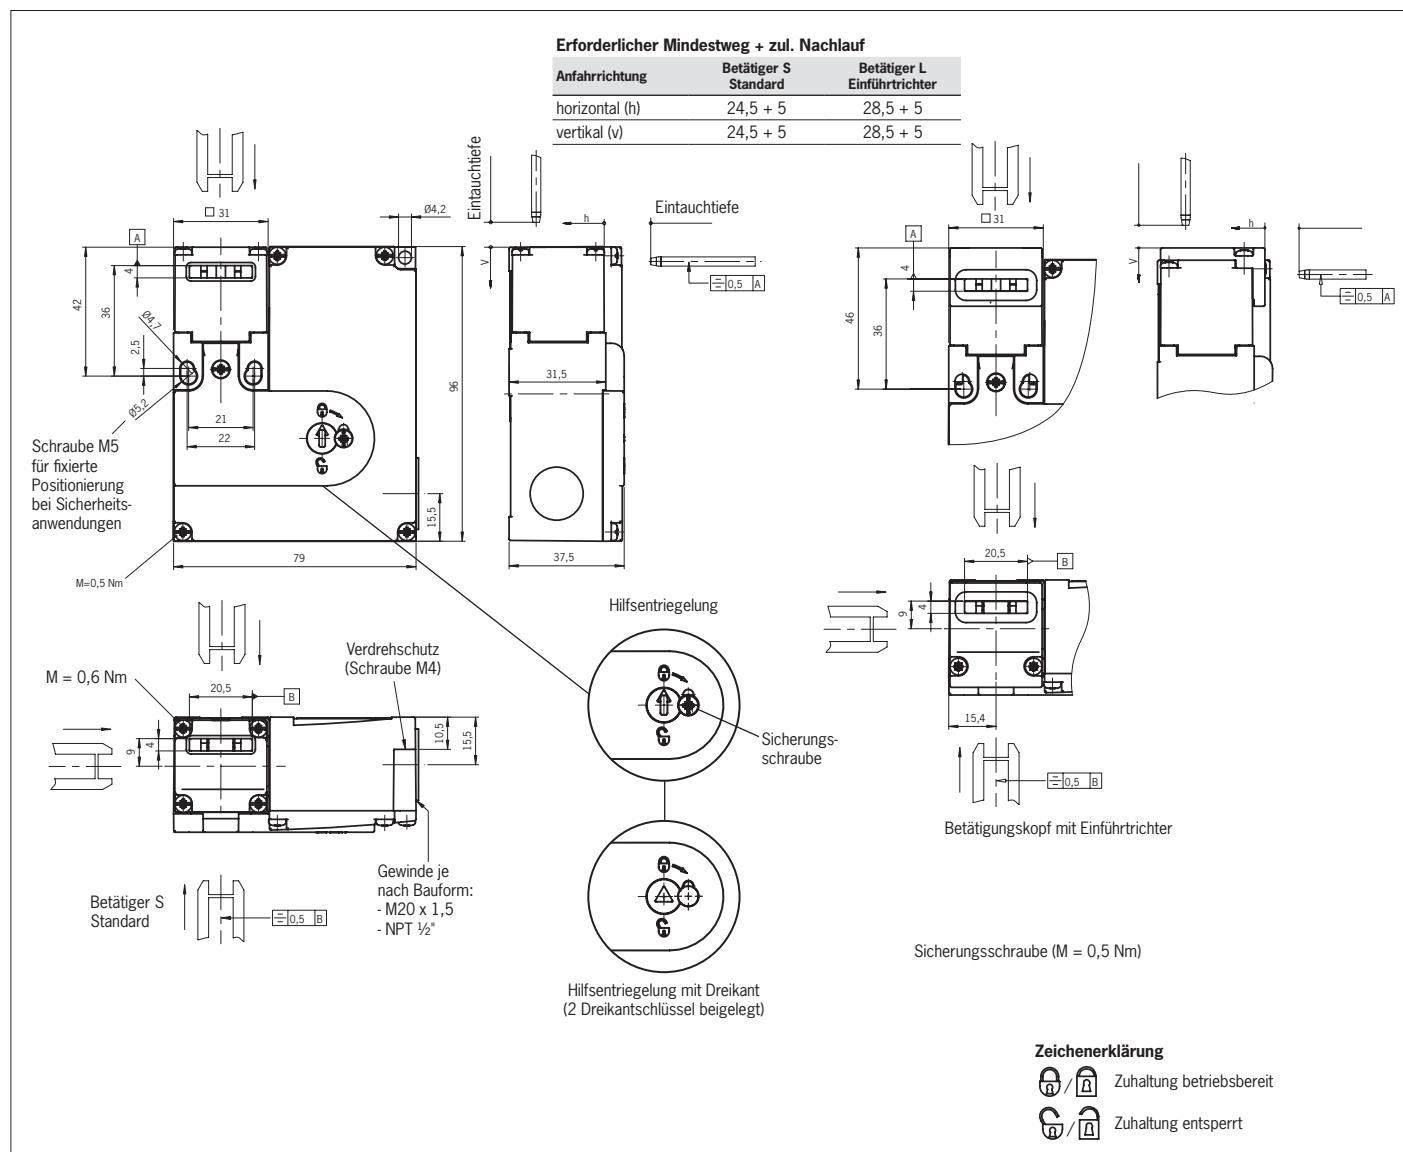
Maßzeichnung STM... ohne Einführtrichter und STM... mit Einführtrichter
